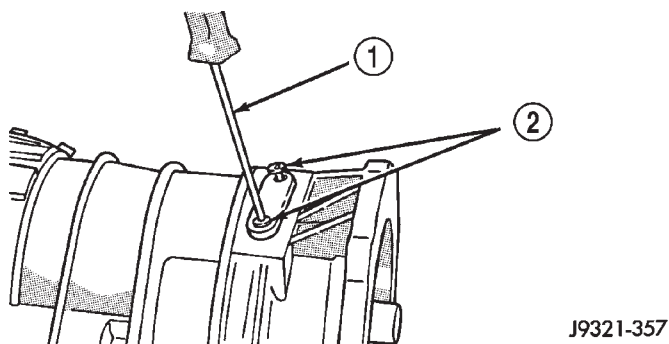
Instalación de la tapa de acceso y la junta del anillo de posición
